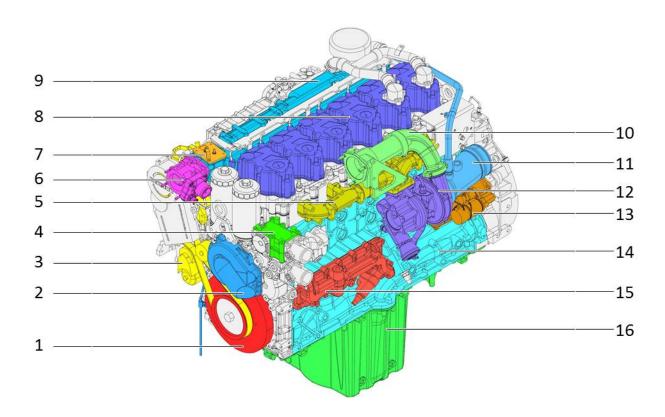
Componentes del motor diésel D936 A7 SCR / Vista de la izquierda delante
